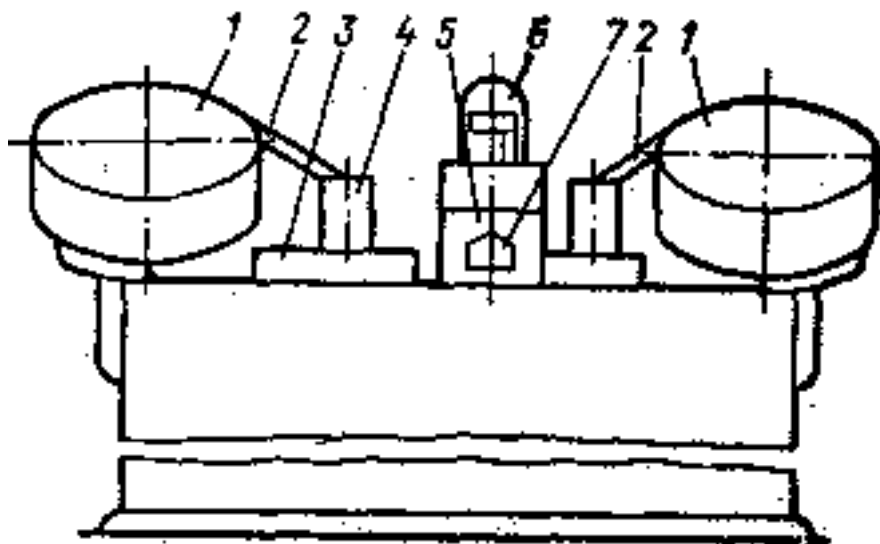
Схема компоновки однопозиционного сборочного автомата
